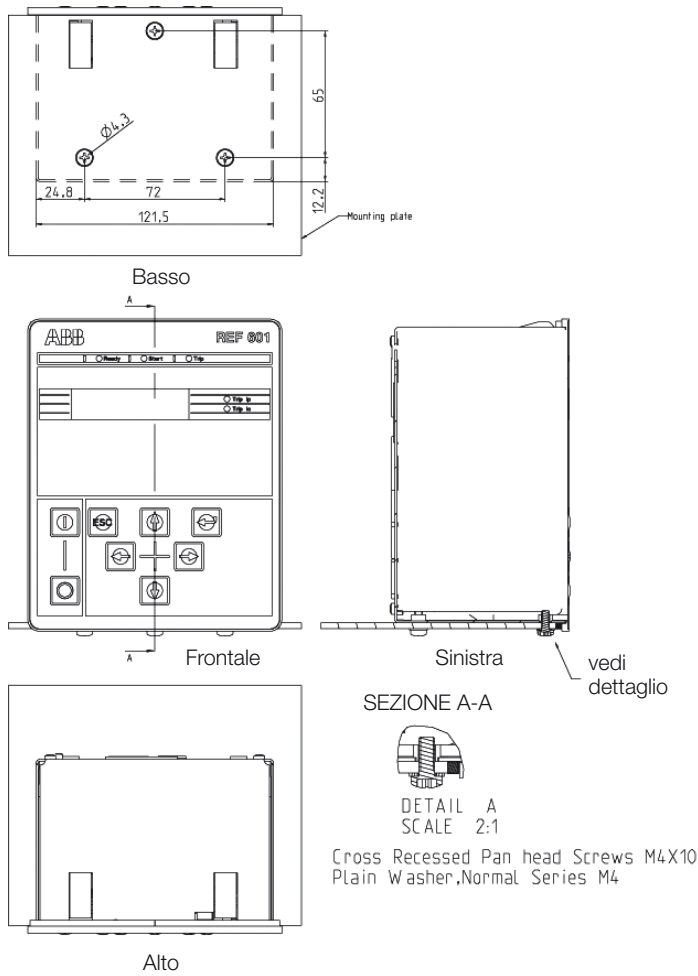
Dimensioni di montaggio del relè da montare sull'interruttore
